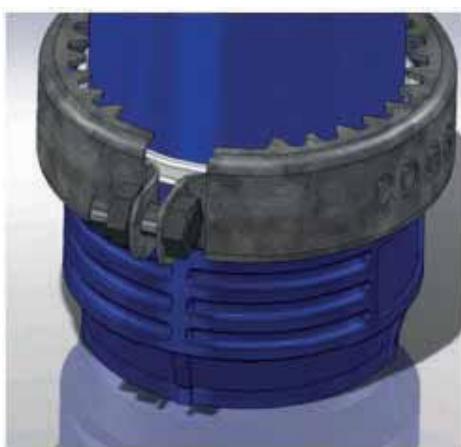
collare antisfilamento e posizione di montaggio sulla giunzione tubo-bicchiere.
